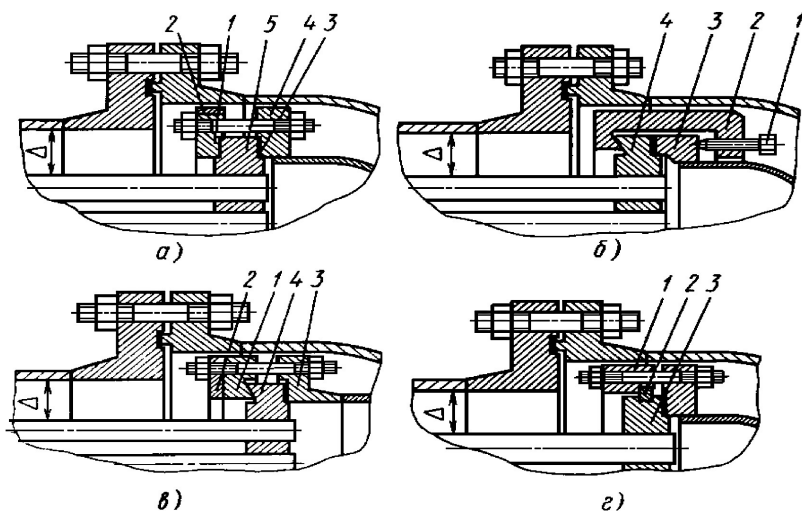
Способы крепления крышки плавающей головки к трубной решетке: а — разрезным фланцем; б — разрезной фланцевой скобой; в — разрезным кольцом; г — разрезным стяжным кольцом
